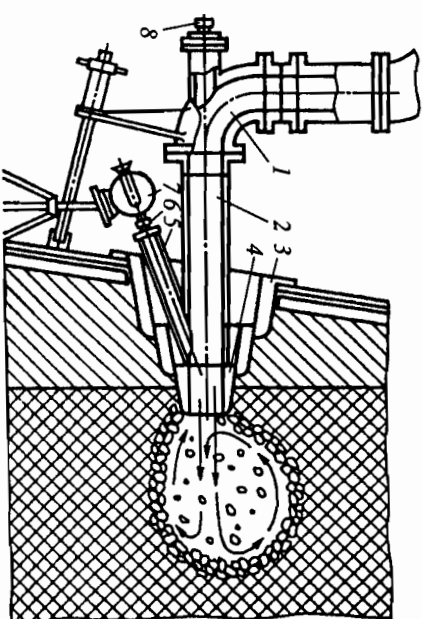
Фруменный прибор и схема зоны циркуляции кокса
